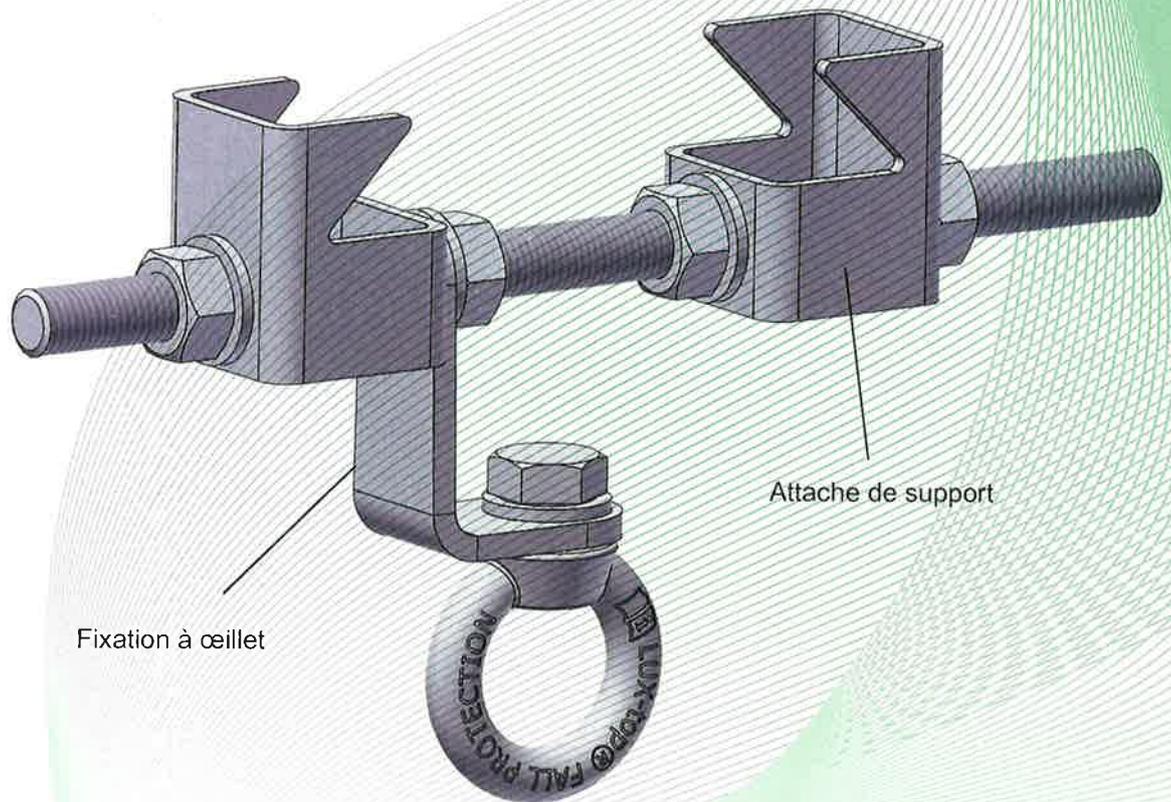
Dispositif d'ancrage, type : LUX-top® QUICKFIX II
